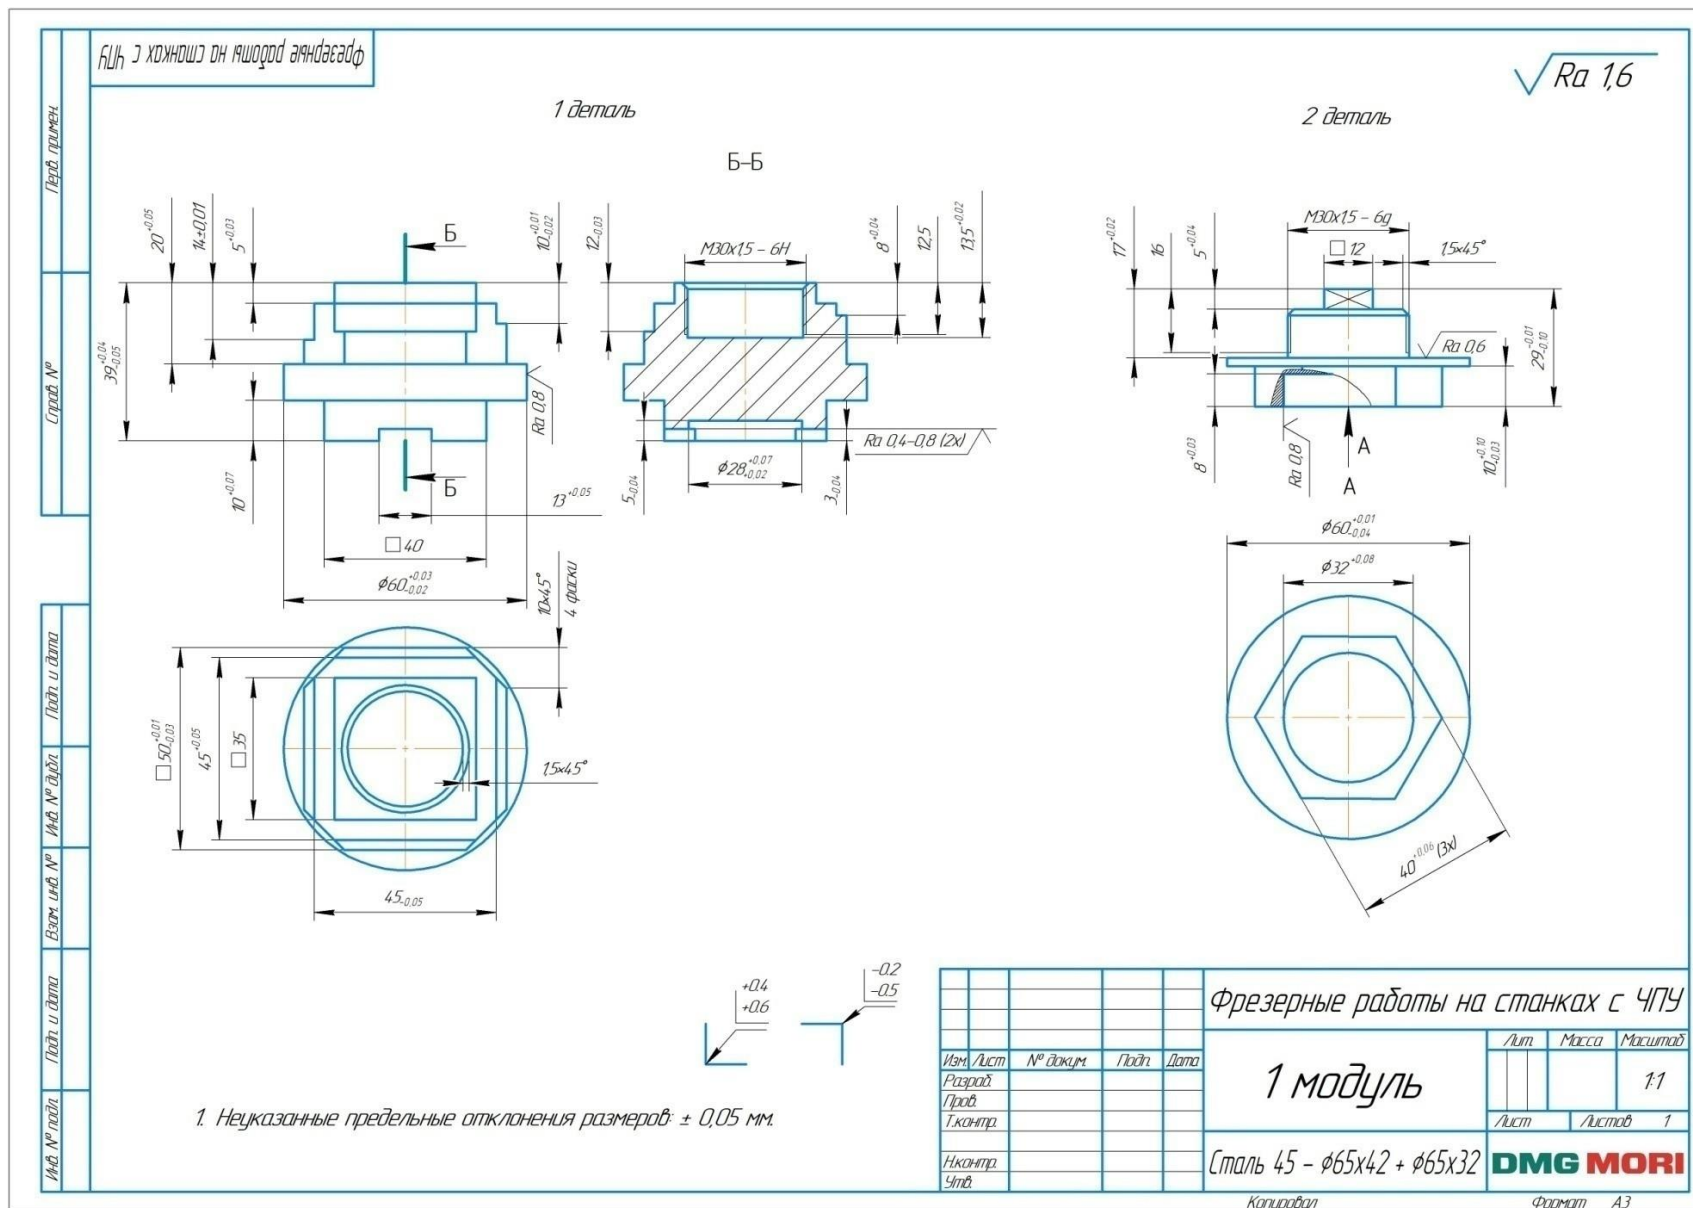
Модуль 1 Сборочный чертеж Фрезерные работы на станках с ЧПУ
